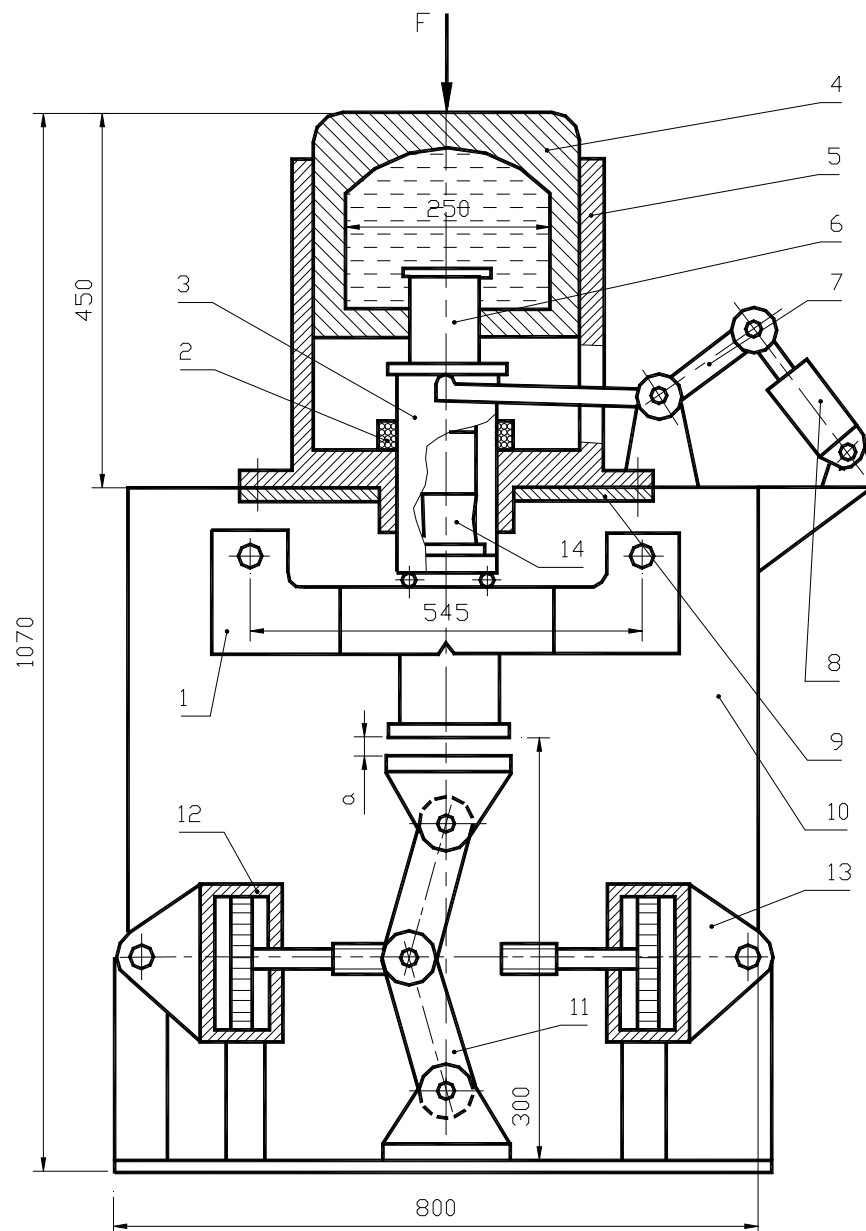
Устройство с гидроаккумулятором энергии упругой деформации для испытания образца: 1 – образец; 2 – гаситель удара; 3 – пуансон; 4 – гидроцилиндр – накопитель энергии; 5 – корпус для установки гидроцилиндра; 6 – шток гидроцилиндра; 7 – шарнир; 8 – пневмоцилиндр; 9 – опорная плита; 10 – стойки; 11 – шарнир; 12 и 13 – пневмоцилиндры; 14 – динамометр
